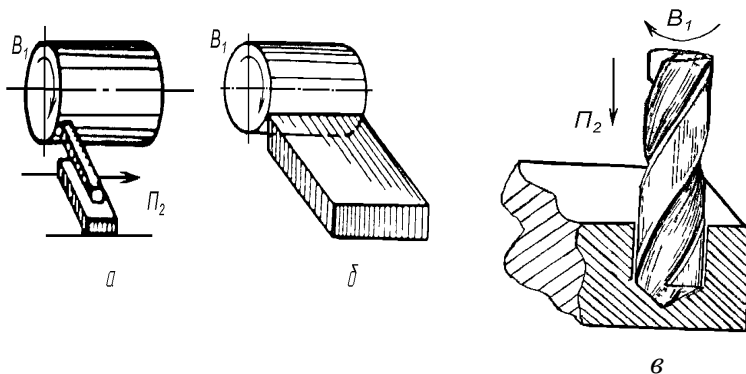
Методы формообразования поверхностей на токарных станках: *а* - двойного следа; *б* – копирования и следа; *в* - двойного следа
